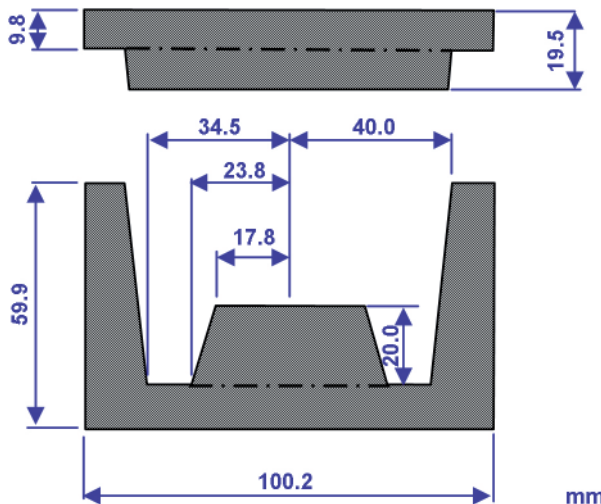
Vista lateral de la caja cilíndrica utilizada como modelo para fabricar el molde de arena.
